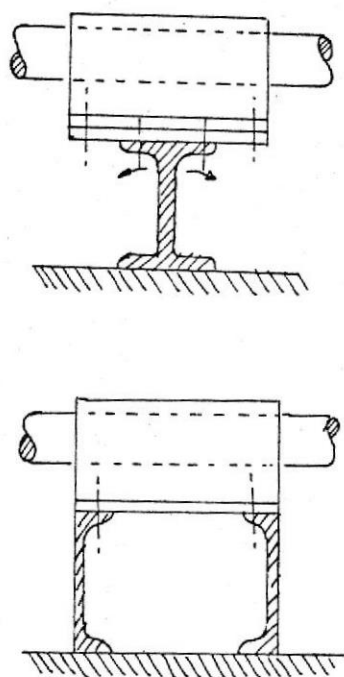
Estructura de Apoyo para Cojinetes
